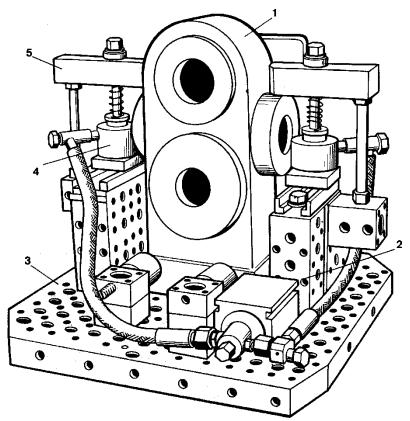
20 Гидравлическое приспособление для установки корпусной детали: 1 - заготовка, 2 - планка, 3 - плита, 4 - гидроцилиндр, 5 - прихват
